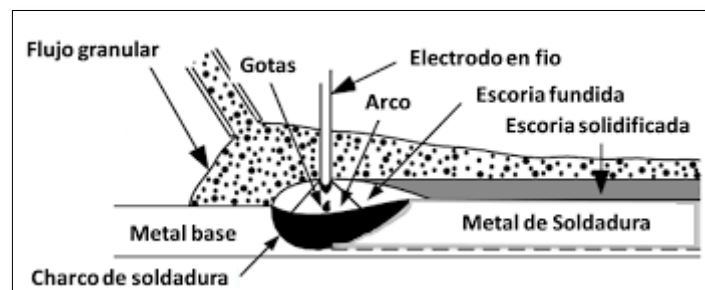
Soldadura por arco sumergido (SAW).
